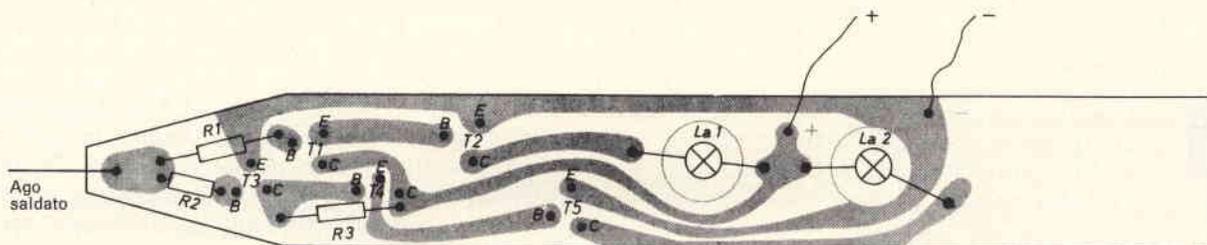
Assemblaggio dei componenti dell'indicatore L-H per frequenze di impulsi rettangolari sino a 60 kHz.
